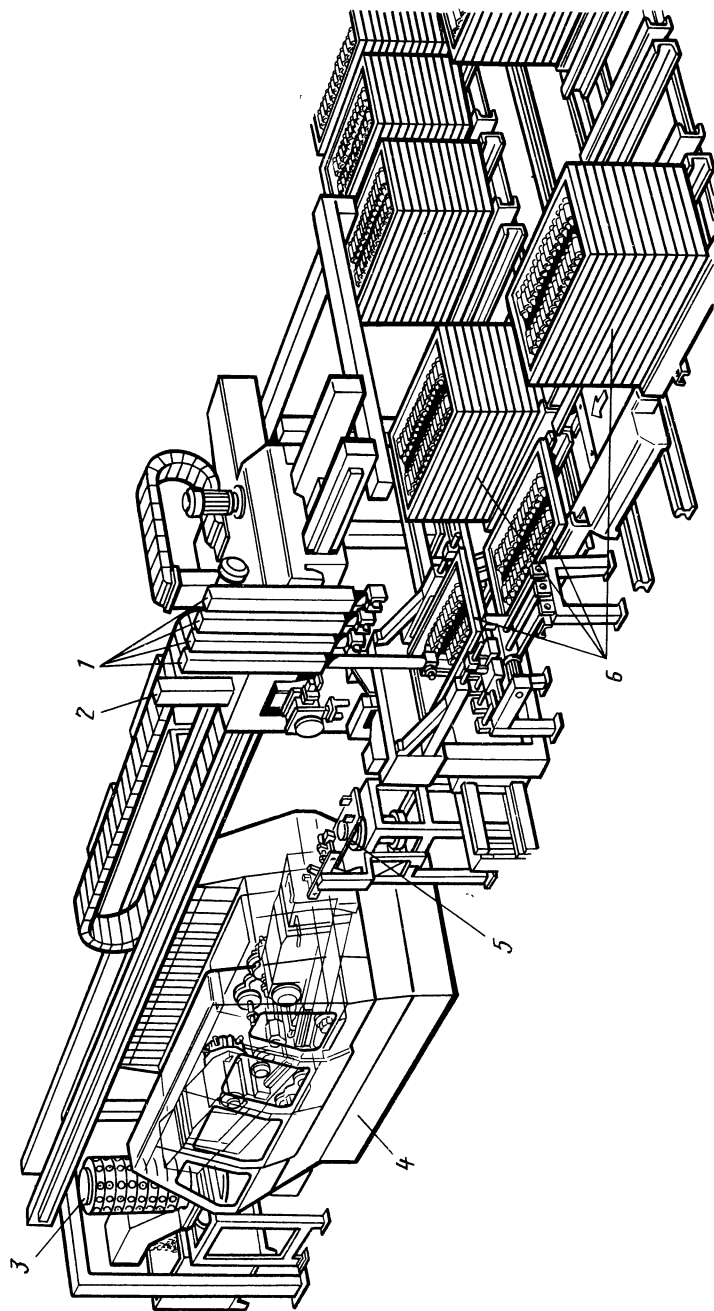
ГПМ на базе двухшпиндельного токарного станка с ЧПУ:
